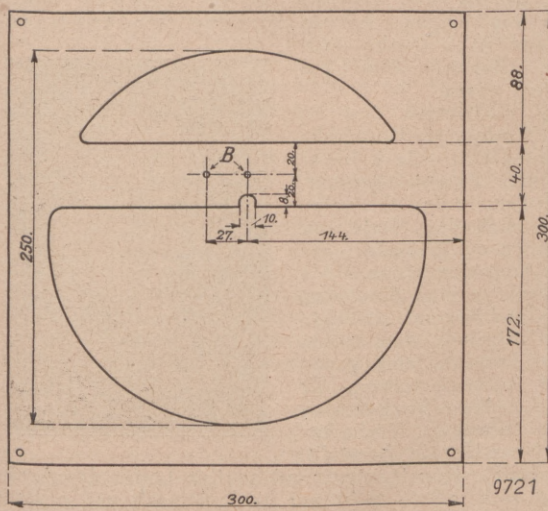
Die Sperrholzmontageplatte für Chassis und System.
